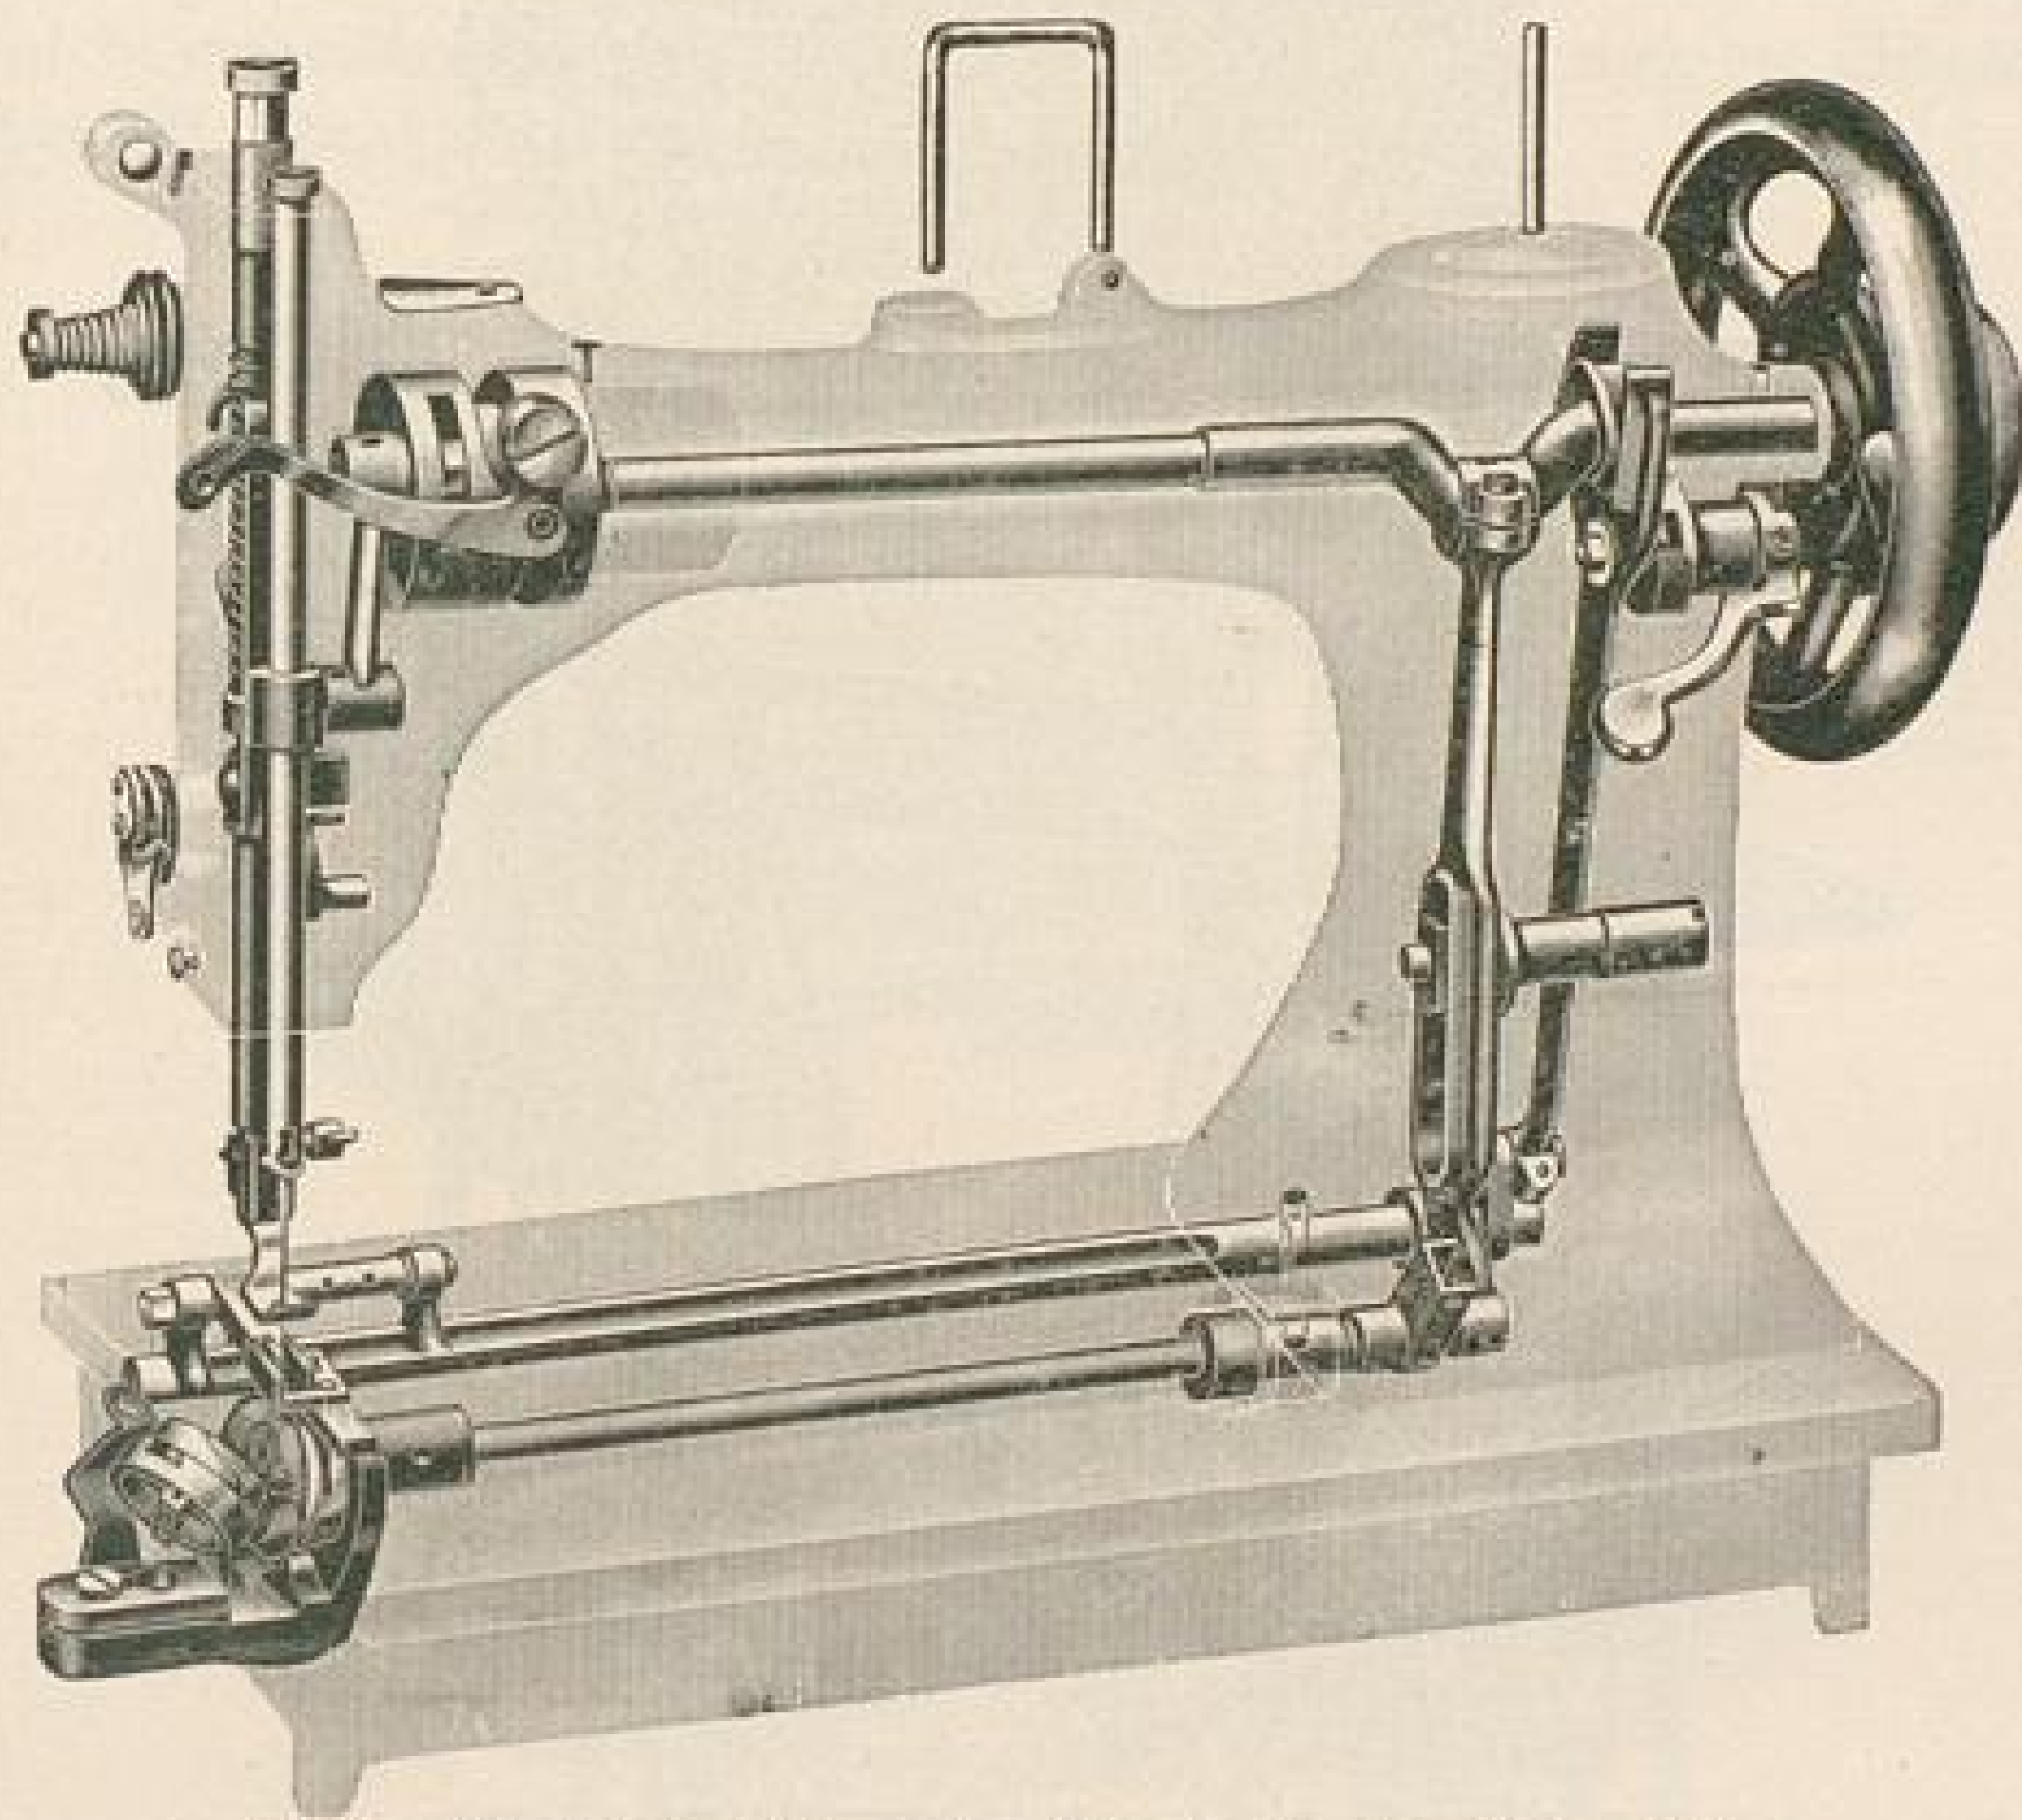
Mechanismus der Phoenix-Greifser-Nähmaschine.
